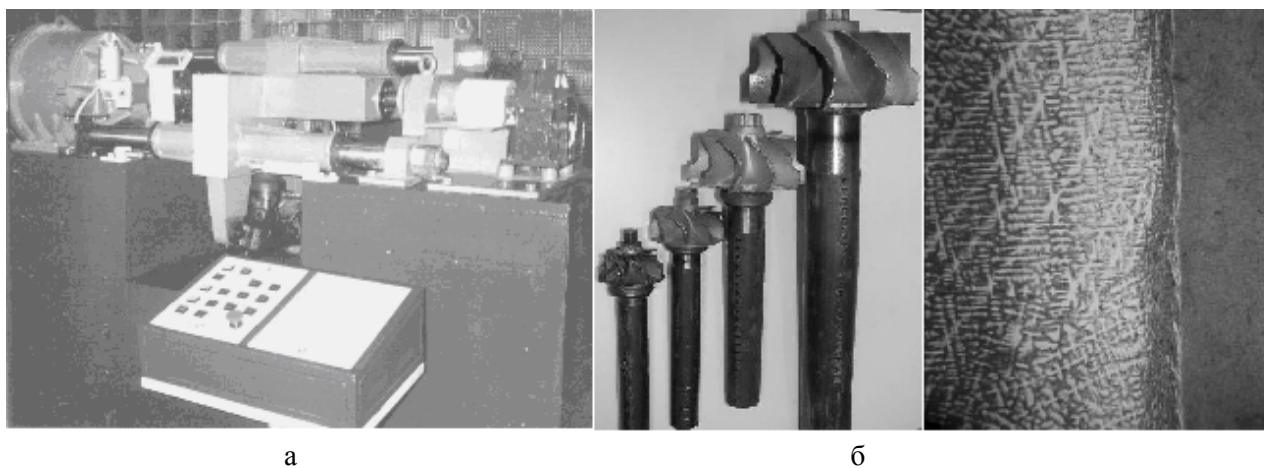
Модернізована установка СТ109А для зварювання тертям (а), зварні вали ротора ТКР (б)
